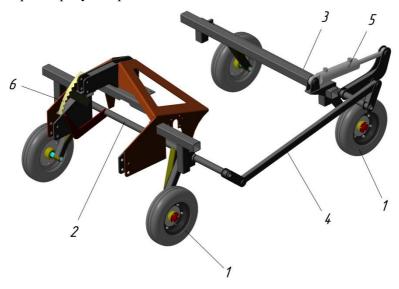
Опорные колеса 1 — колесо (шина 5x10); 2 — ось передняя; 3 — ось задняя; 4 — тяга; 5 — гидроцилиндр Ц.80.40.250; 6 — линейка.
